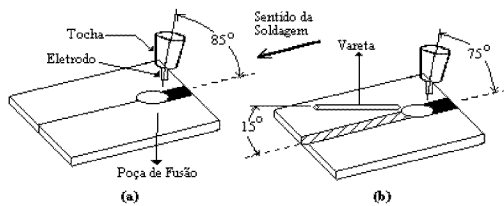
Técnicas para a Soldagem a Topo TIG: (a) Sem e (b) Com Metal de Adição.
